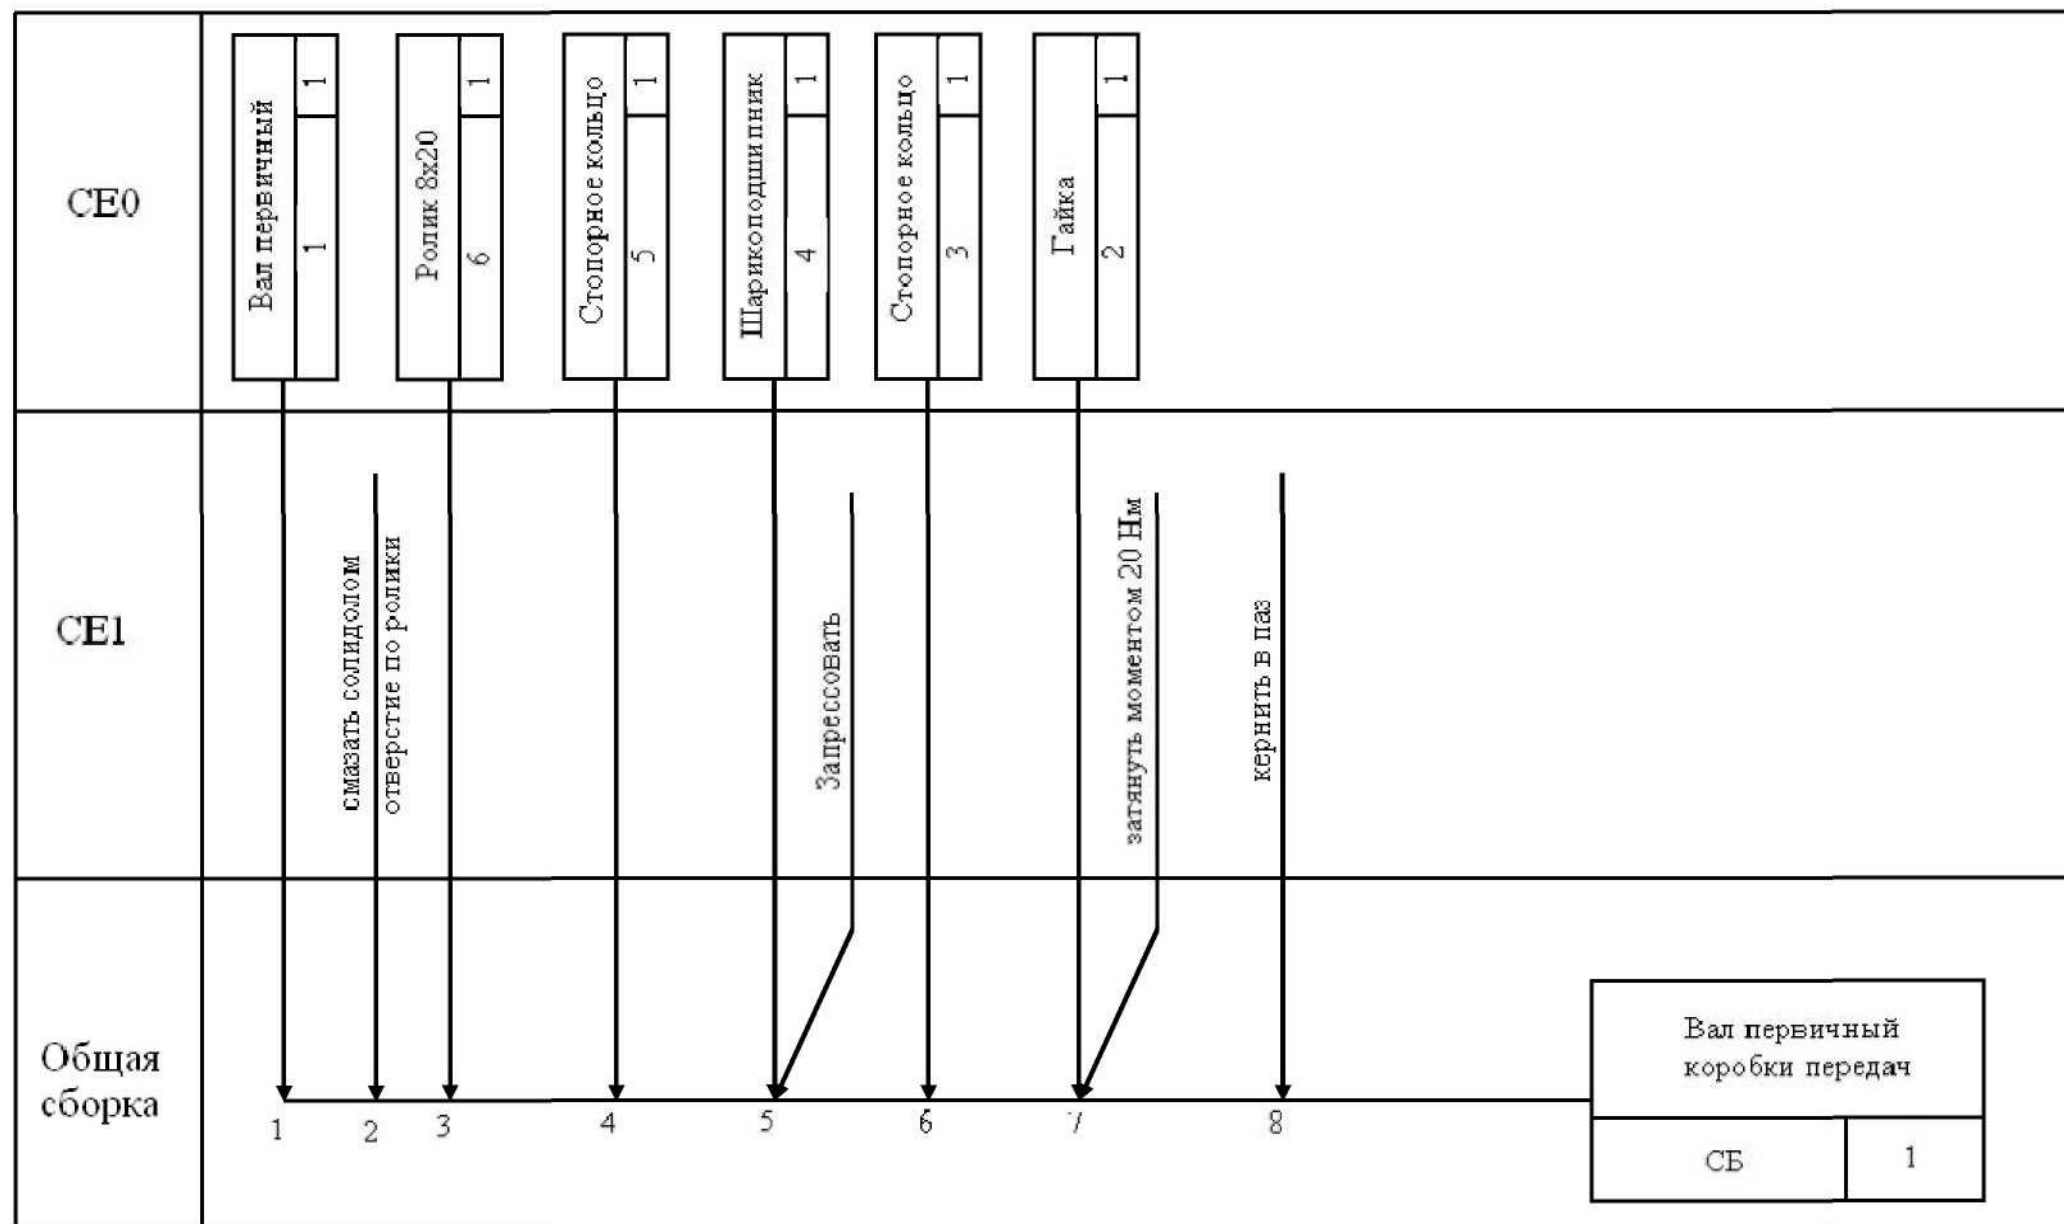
Технологическая схема сборки вала первичного коробки передач
